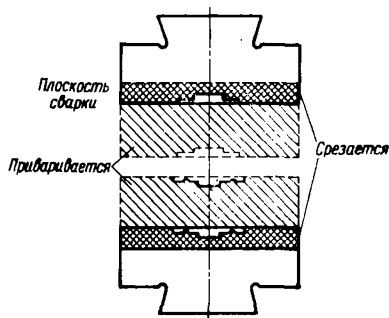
Схема ремонта молотовых штампов электрошлаковой сваркой
